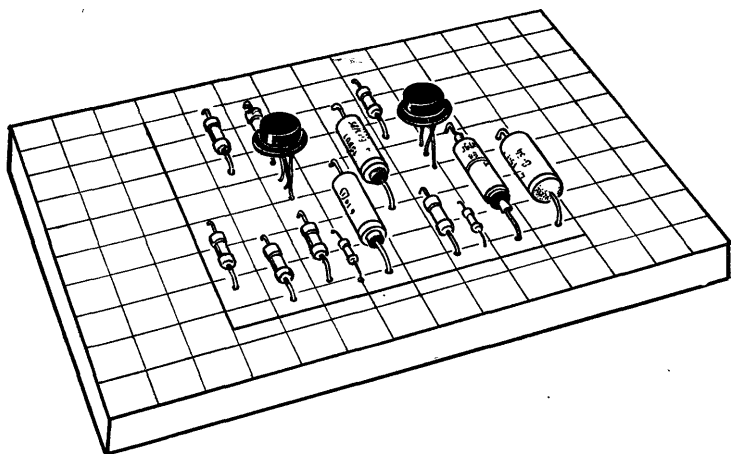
Разработка схемы расположения деталей на пенопласте.
